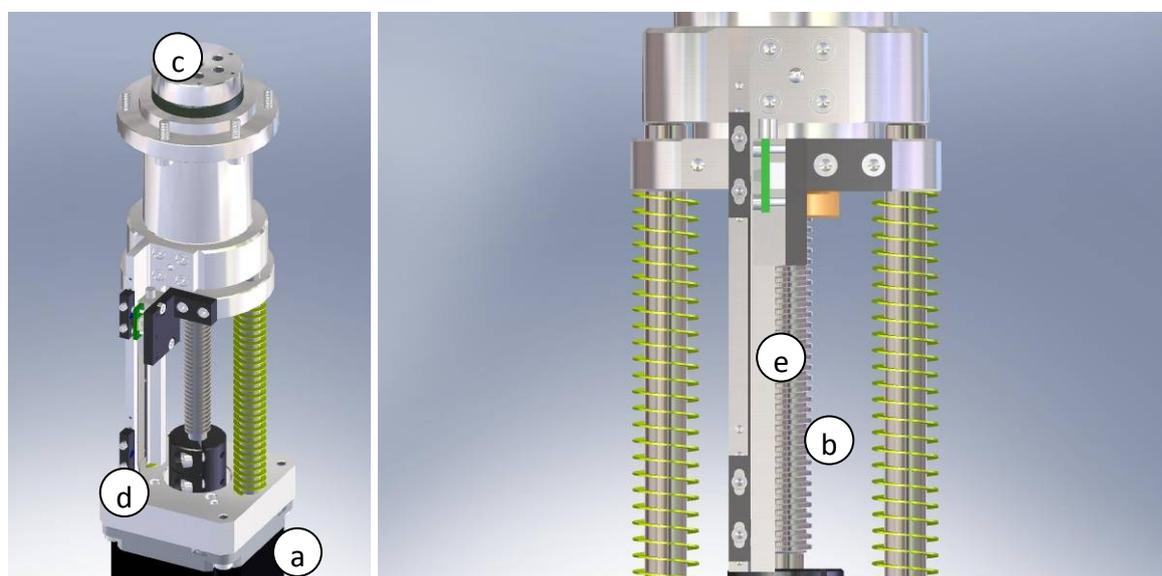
Bewegungseinrichtung der Sinterplattform, a) Motor b) Antriebsspindel c) Plattform d) Maßstabhalter e) Halterung Messsystem
